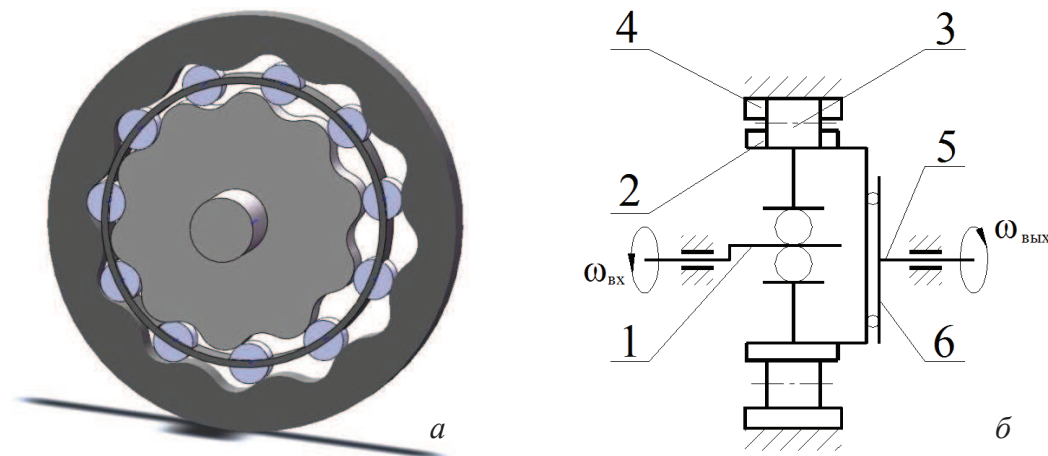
Передача с промежуточными телами качения и свободной обоймой: а) общий вид; б) кинематическая схема
